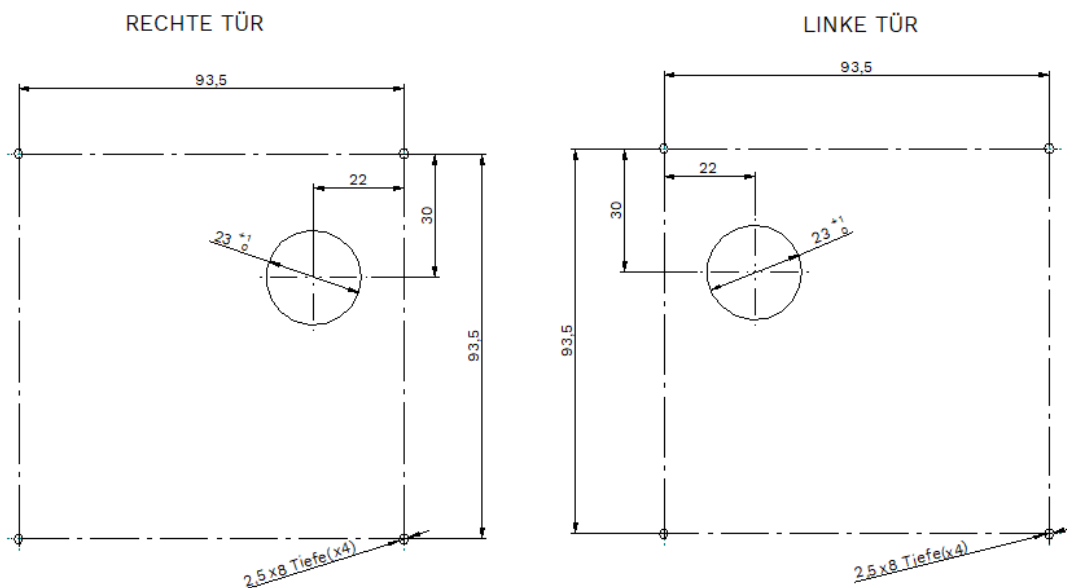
Abmessungen der Befestigungsbohrungen in mm. Holz
